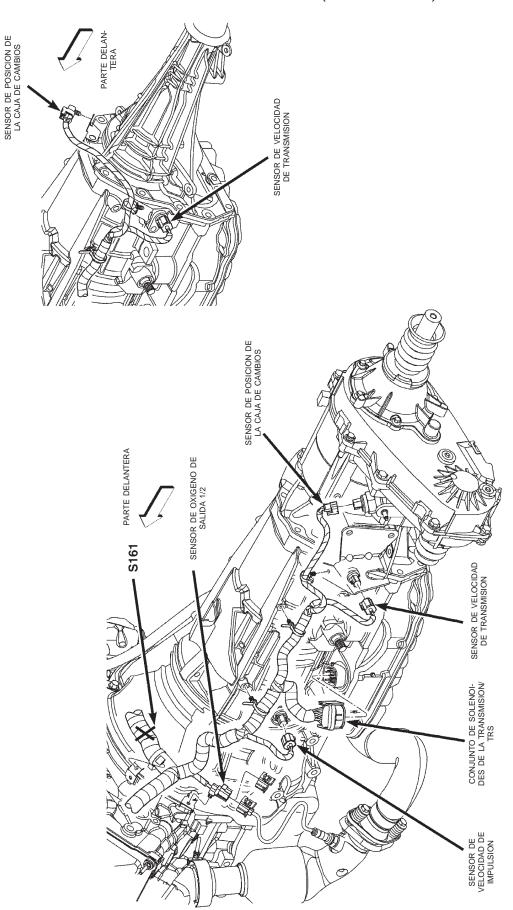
LADO INFERIOR IZQUIERDO DEL MOTOR 3.7L
